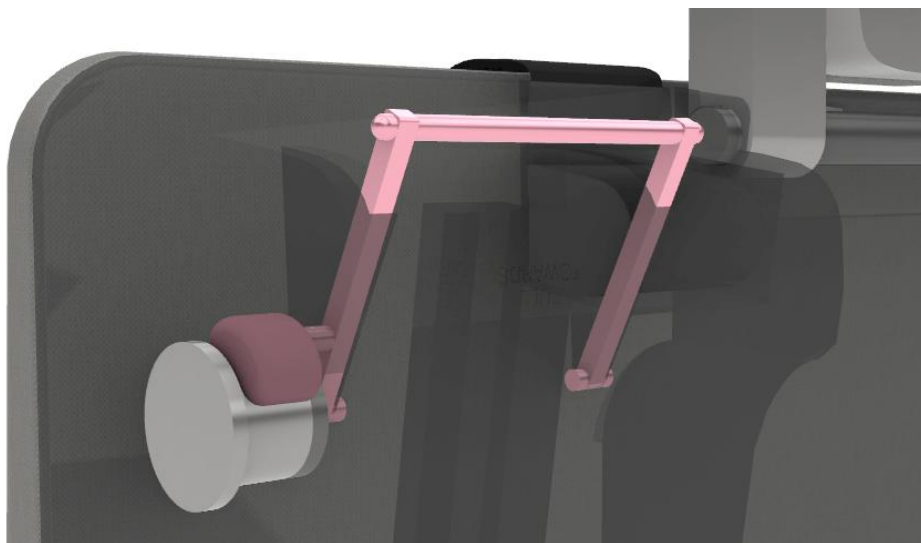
Mechanismus zafixování opěrky hlavy
